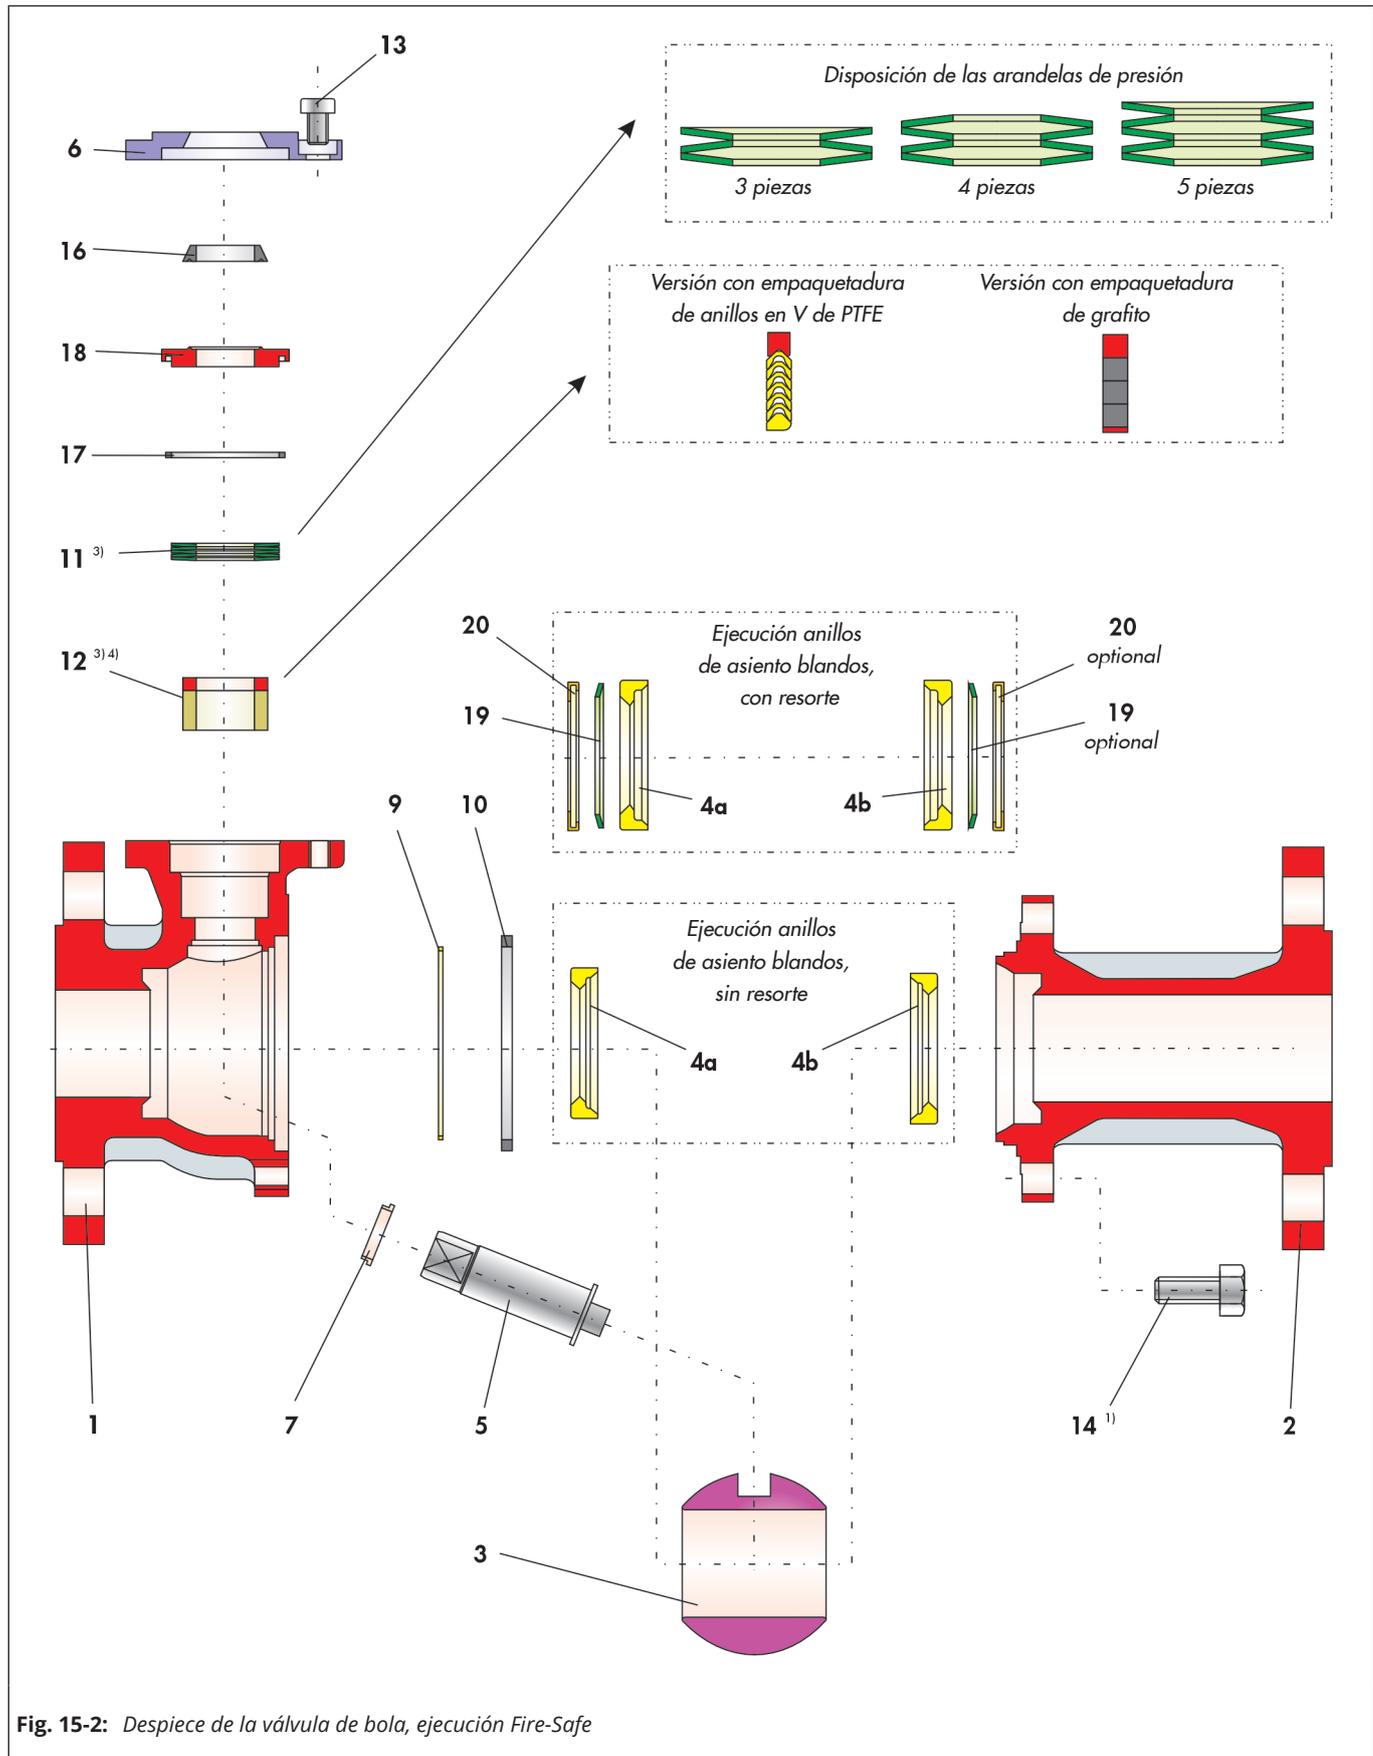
Despiece de la válvula de bola, ejecución Fire-Safe
